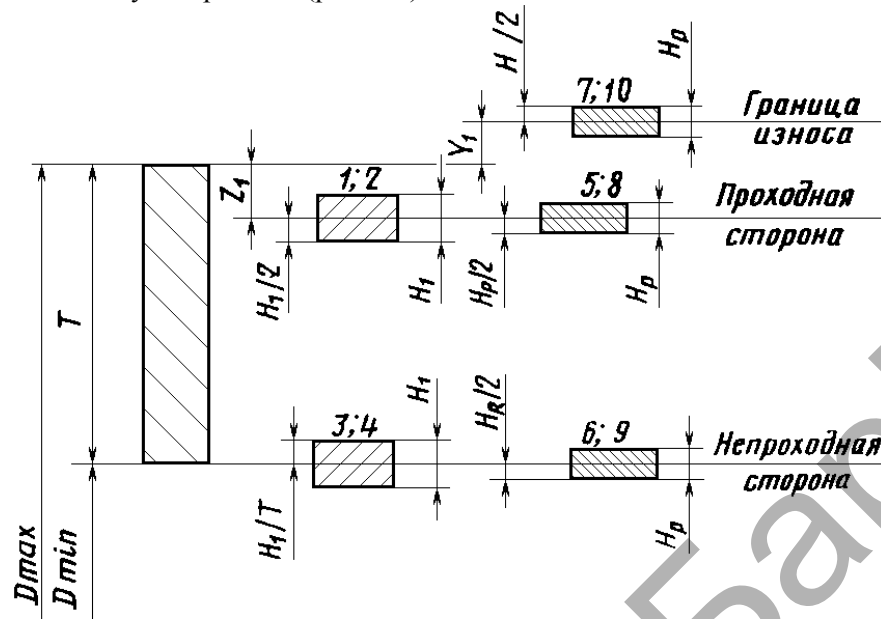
Схема расположения полей допусков калибров и контракалибров для вала из ГОСТ 25346
